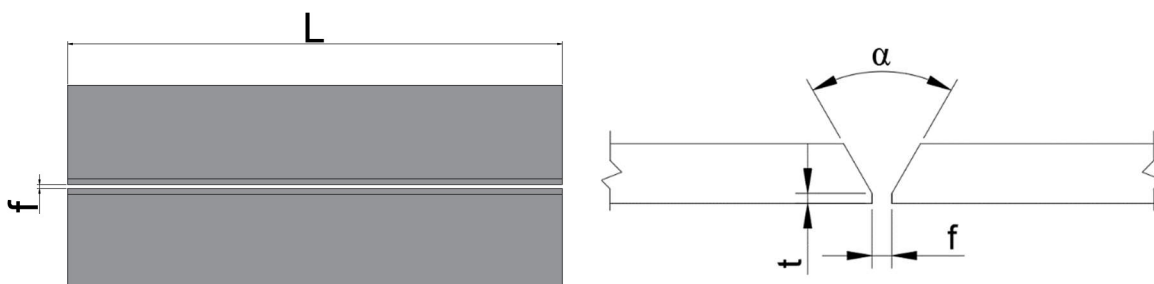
Ilustração esquemática da junta de soldadura utilizada.
